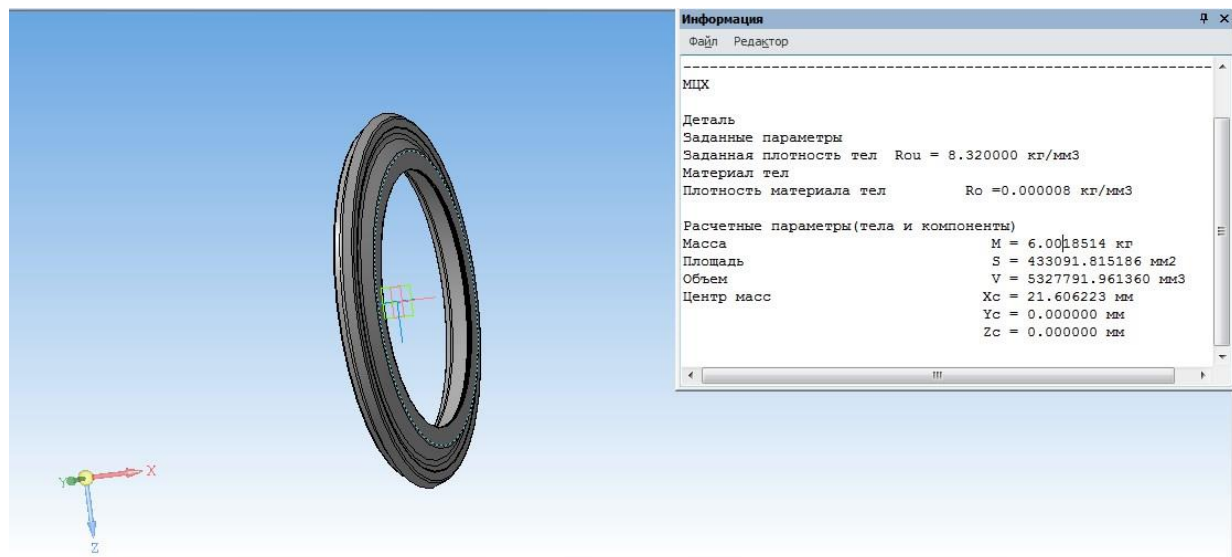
Ескіз заготовки штампування на молотах
